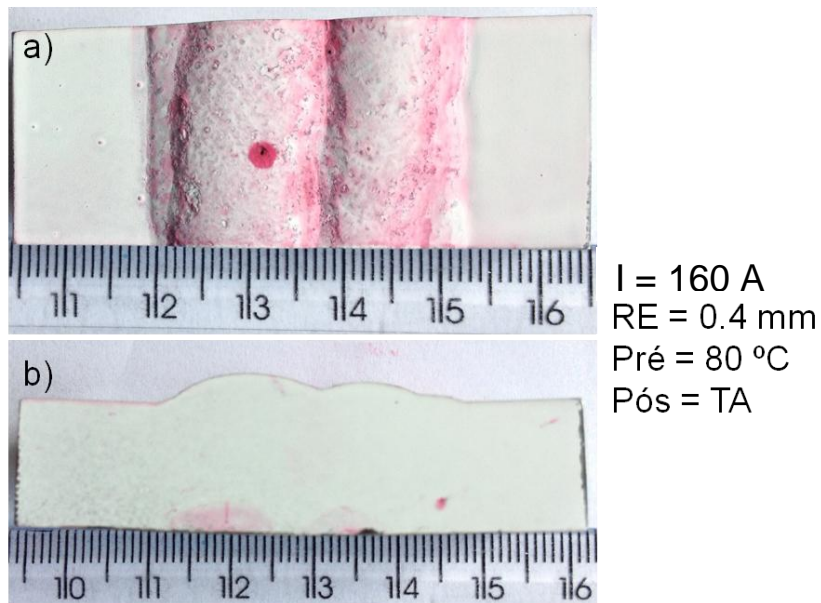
Inspeção visual por líquido penetrantes do CP 1. Em a) vista de topo; em b) vista da seção transversal.
